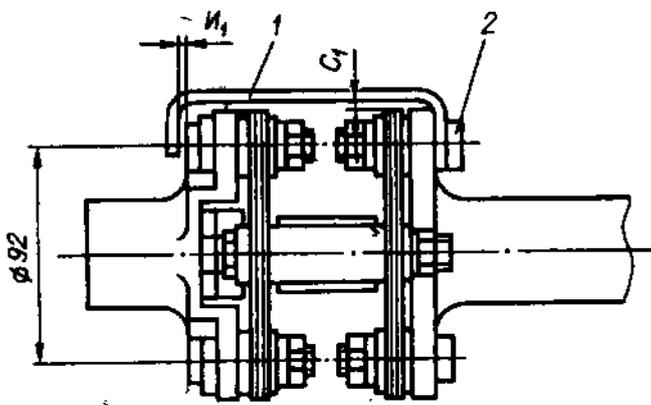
Центровка топливного насоса высокого давления с валом привода:
